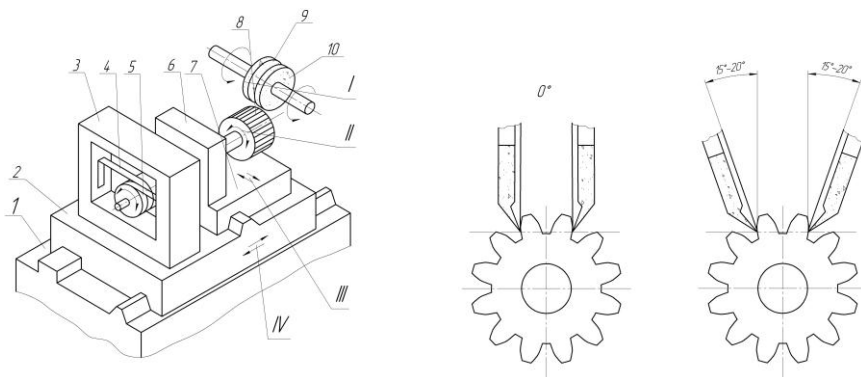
Метод зубошлифования зубчатых колес непрерывной обкаткой двумя тарельчатыми кругами
